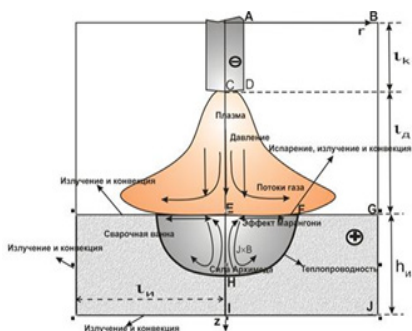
Схема расчетной области дуговой сварки в инертных газах
